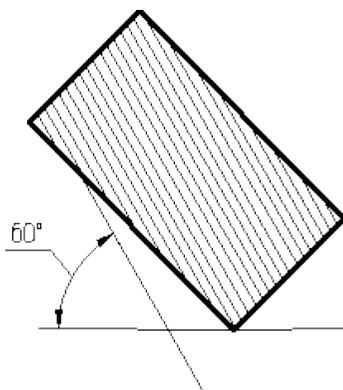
Штриховка под углом 60° к рамке чертежа
